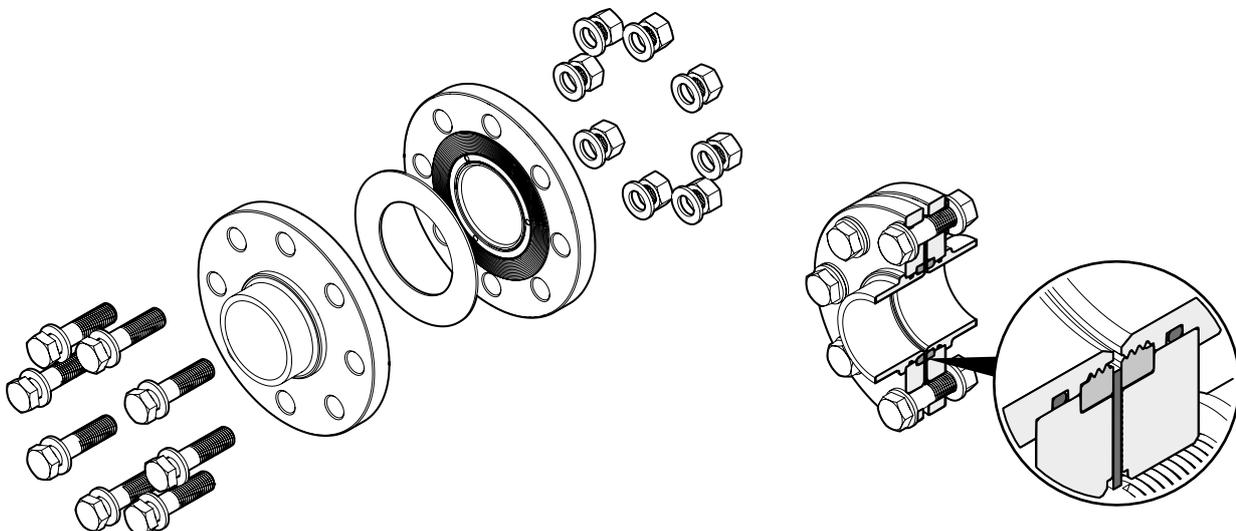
Assemblage par bride tournante (non vissé/vissé)
